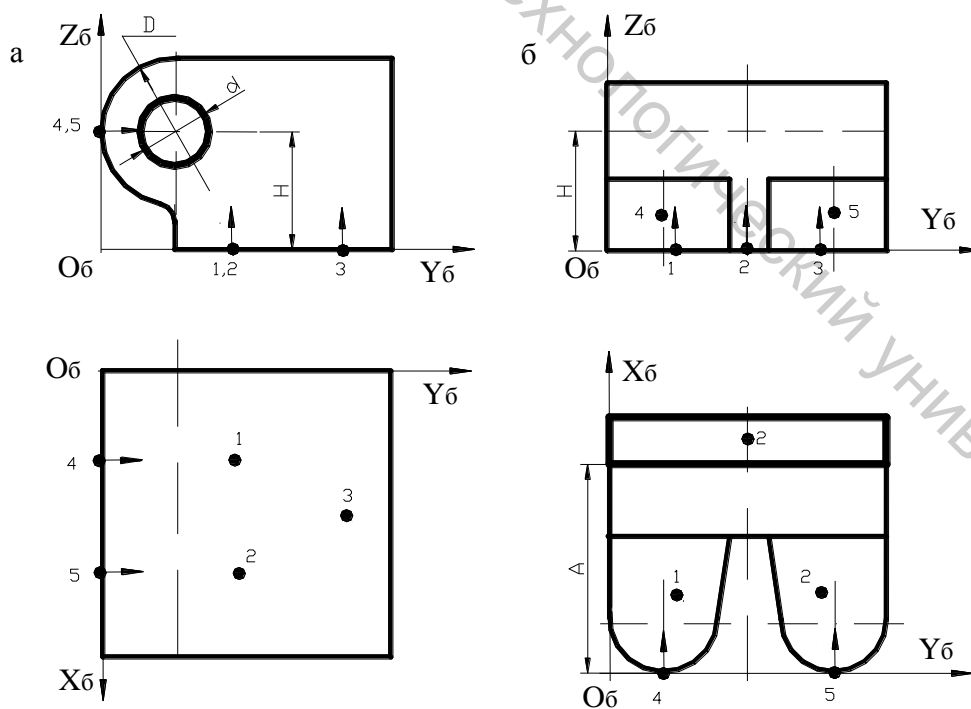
Схема реализации направляющей базы с помощью: образующей цилиндра (а), образующими двух наружных цилиндров (б)
